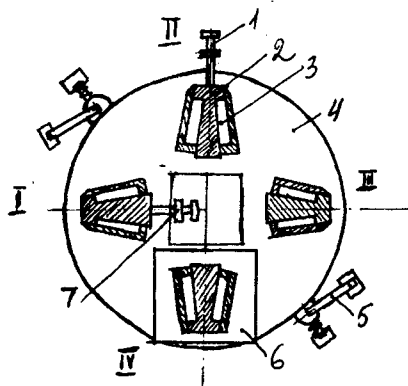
Формовочный ротор: I — пост расформовки блоков; II — пост сборки смазки формы; III — пост заливки смеси; IV — пост вакуумирования
